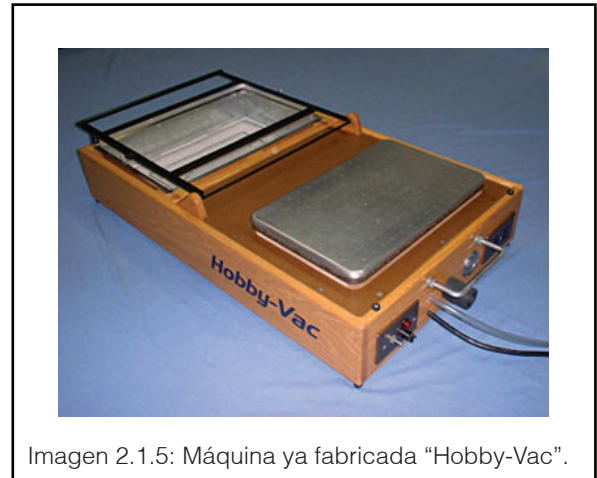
Máquina ya fabricada "Hobby-Vac".
